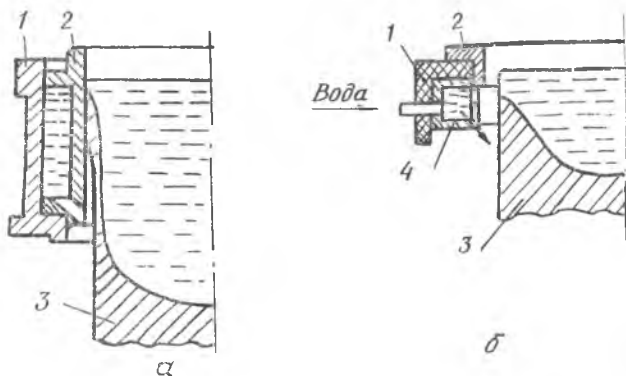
Схема кристаллизатора скольжения — а и ЭМК — б: 1 — корпус; 2 — гильза; 3 — слиток; 4 — индуктор
